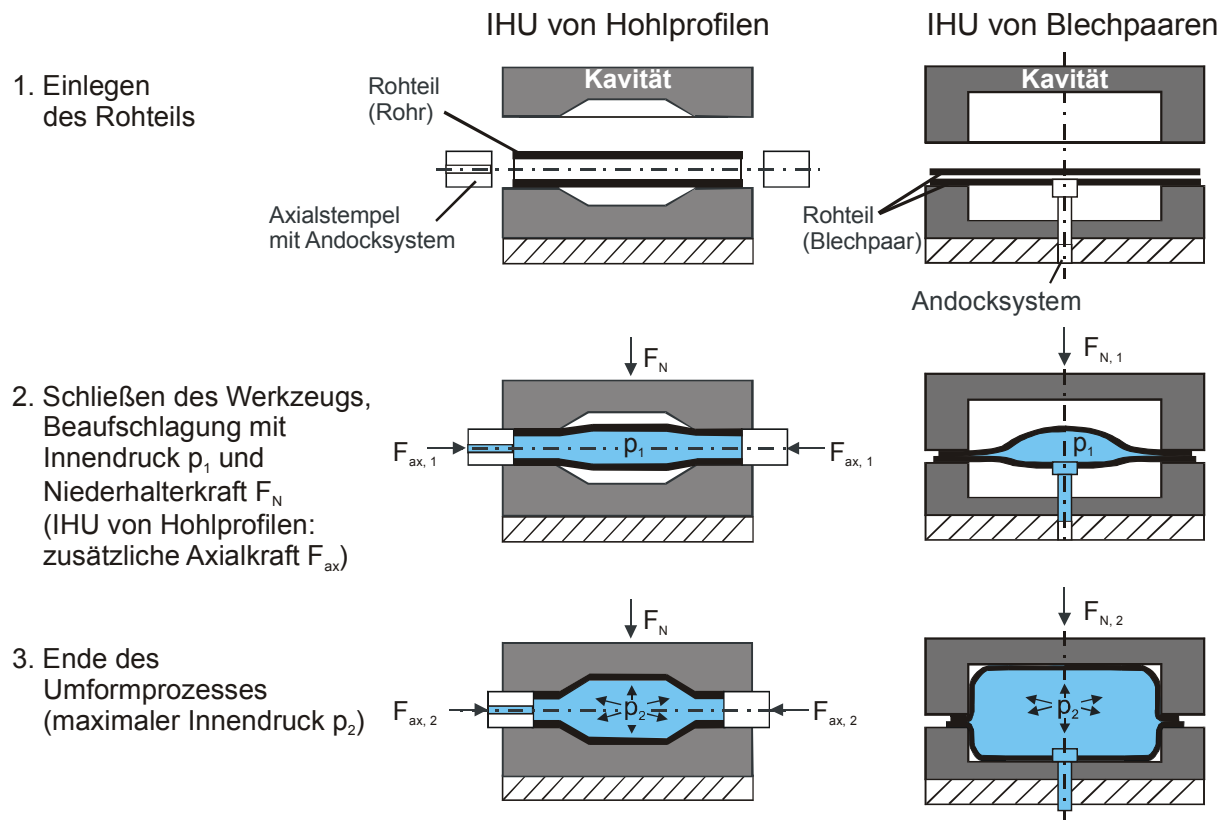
Prinzipieller Verfahrensablauf des IHU von Hohlprofilen und unverschweißten Blechpaaren
